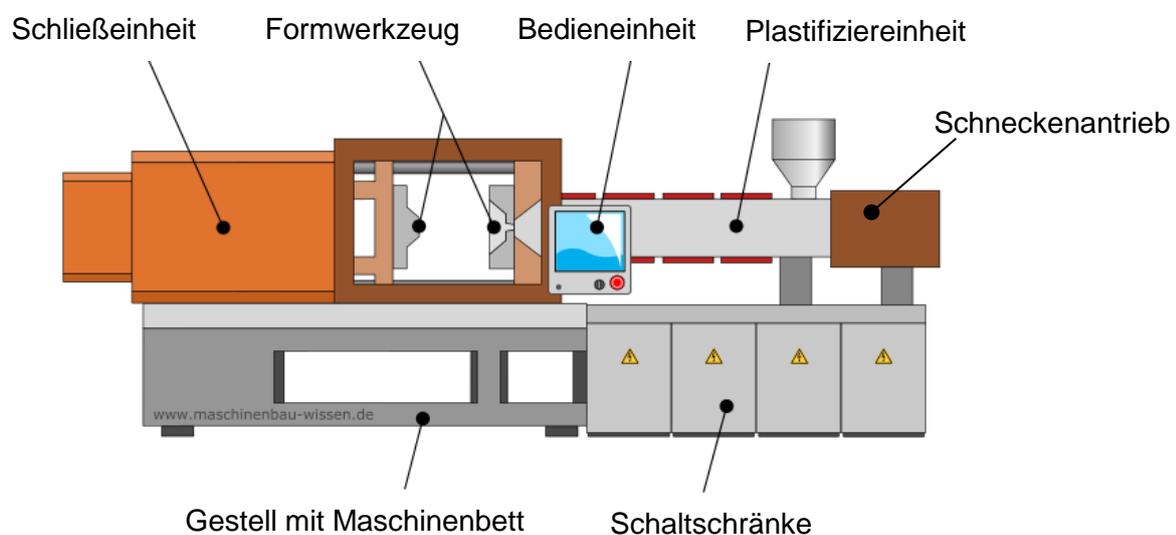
Die Hauptkomponenten einer Spritzgießmaschine [6]
